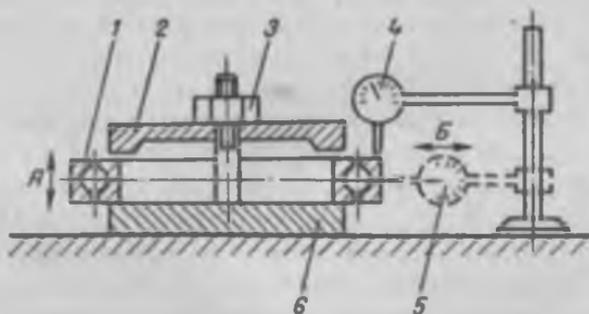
Приспособление для определения зазоров в подшипнике
